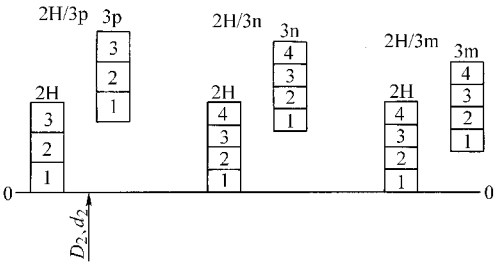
过盈配合螺纹中径公差带分组位置
